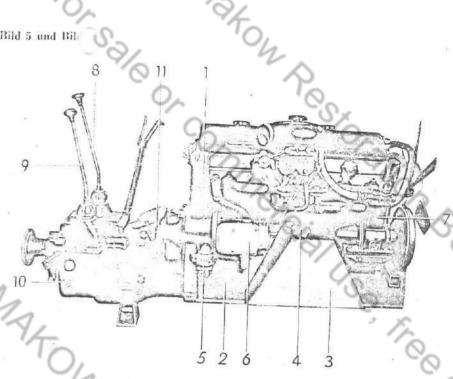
Motor mit Wechselgetriebe, Ansicht von rechts .
